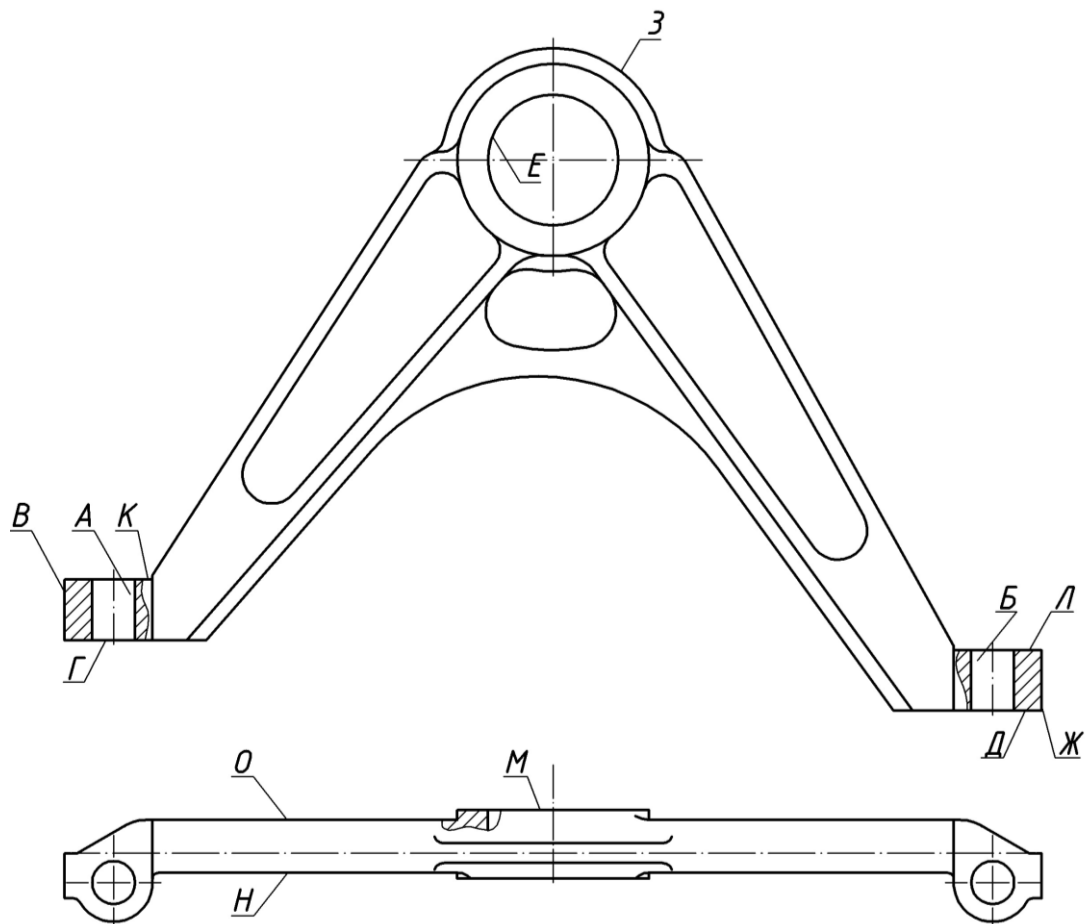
Ескіз о деталі 65-20027 з позначеними поверхнями
